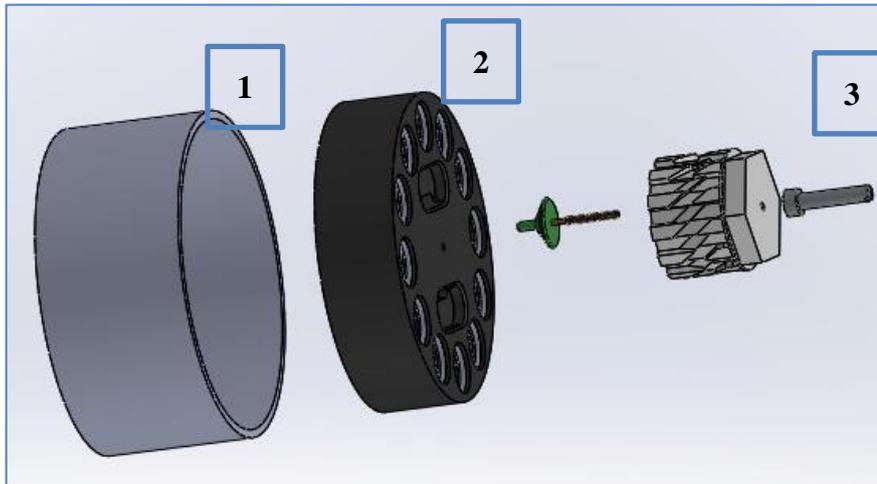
Diseño mecánico propuesto – Instalador de Calibradores
